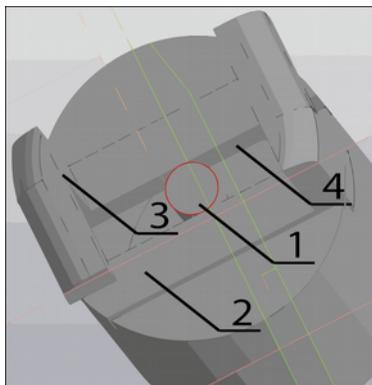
Структур захвата: сжимающие поверхности (3), рельсы (2), зубцы на внутренней стороне (4); между зубчатыми поверхностями расположена шестерня (1)
